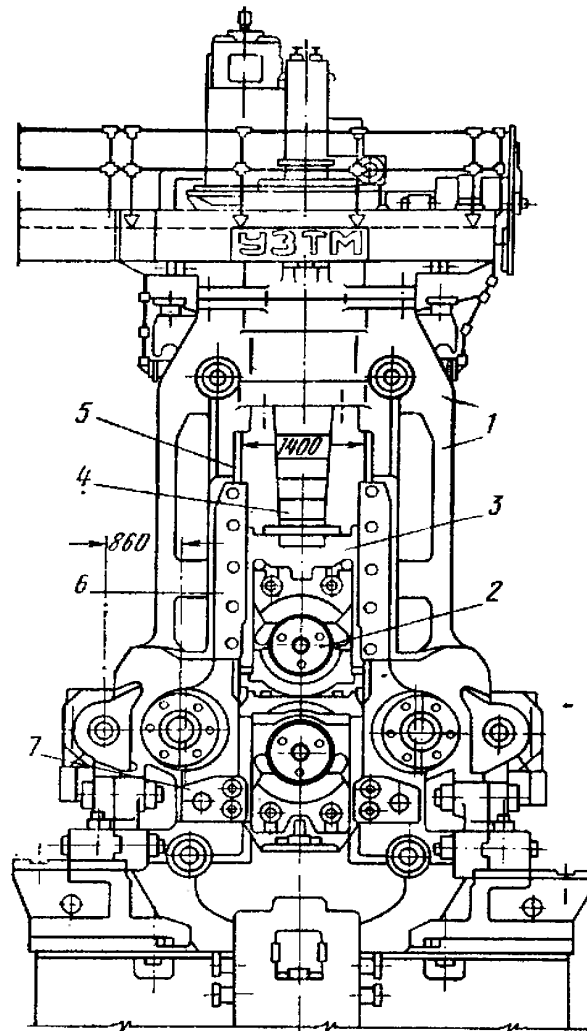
Загальний вигляд двох валкова робочої кліті блюмінга
